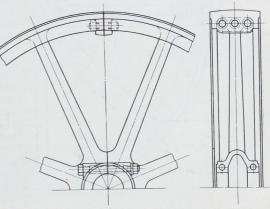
Zwischen den Armen geteiltes, an der Fuge bearbeitetes Rad.
